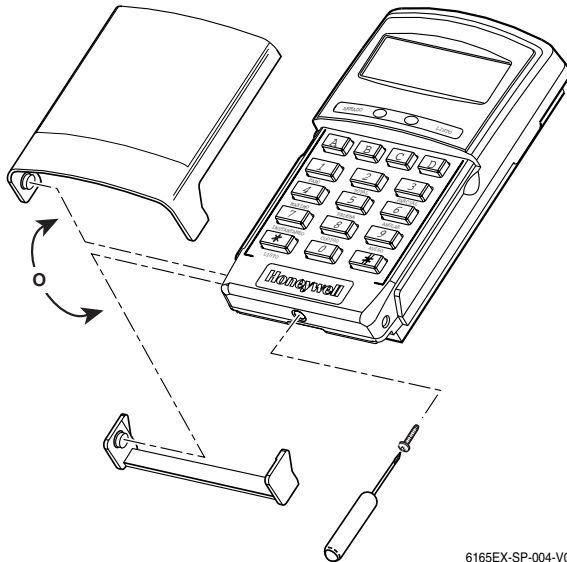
Cierre del teclado (se muestra sin la tapa frontal)
